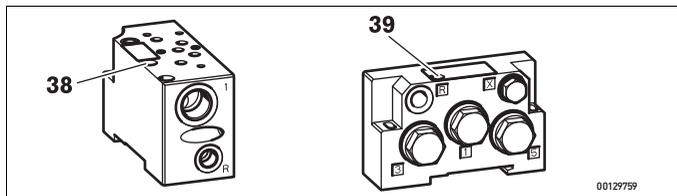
MS01-AL, Bohrungen für Befestigung auf Hutschiene
